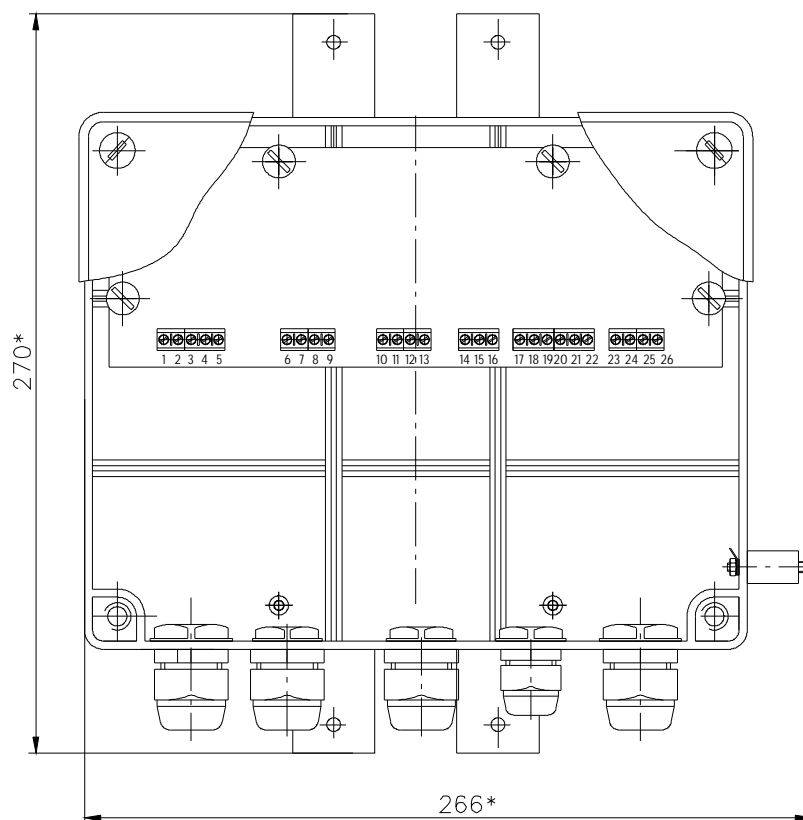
Внешний вид коробки КК-1. Крышка не показана.
